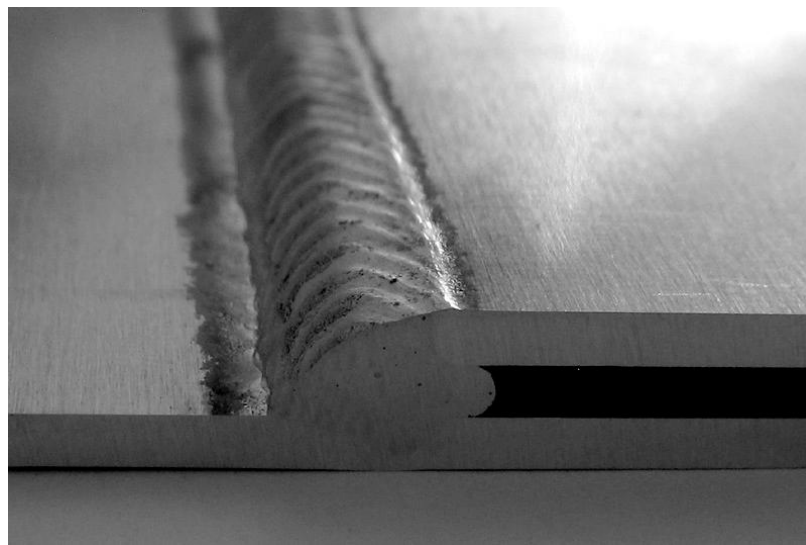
Smíšený spoj ocel-hliník [5]
